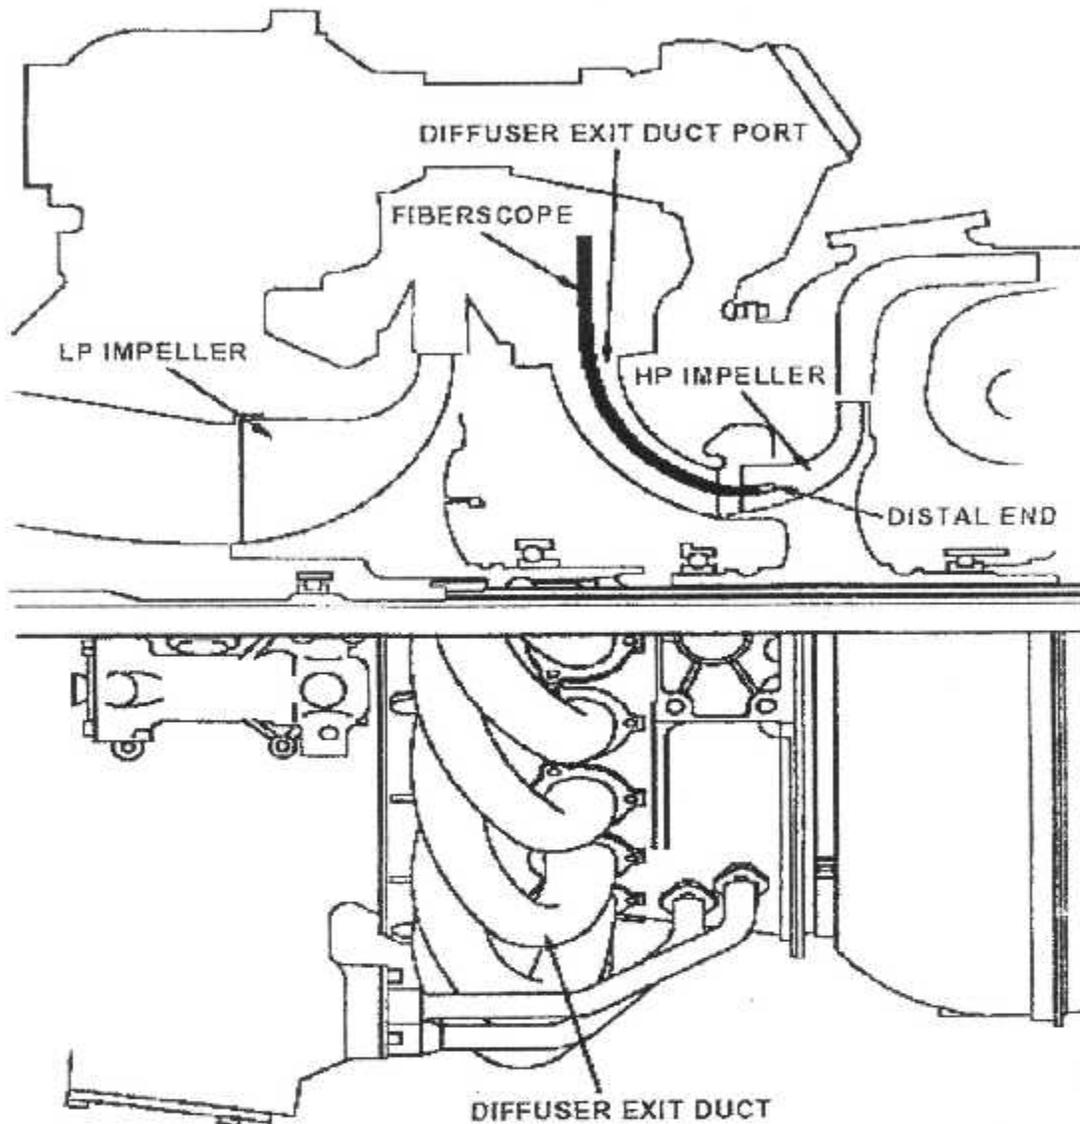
Inspection boroscopique du compresseur HP.
